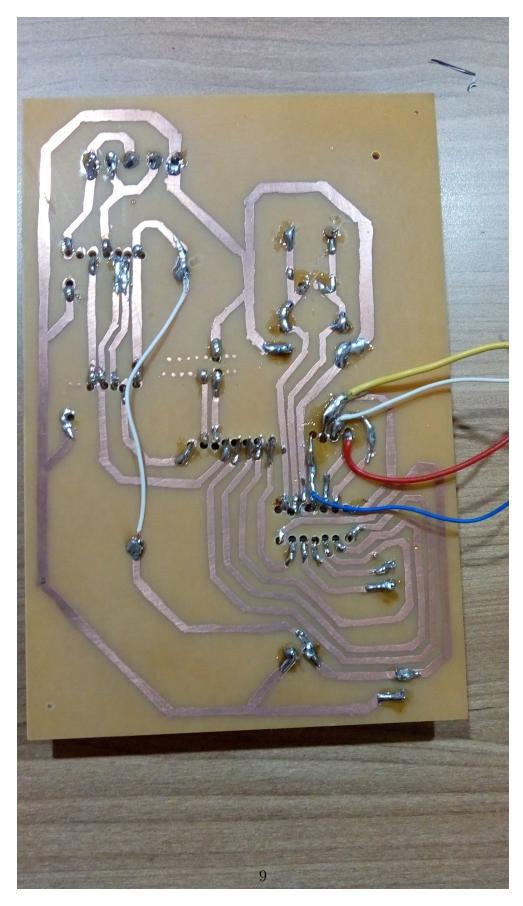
Placa final vista de baixo, enfatizando o roteamento e a soldagem dos componentes.
